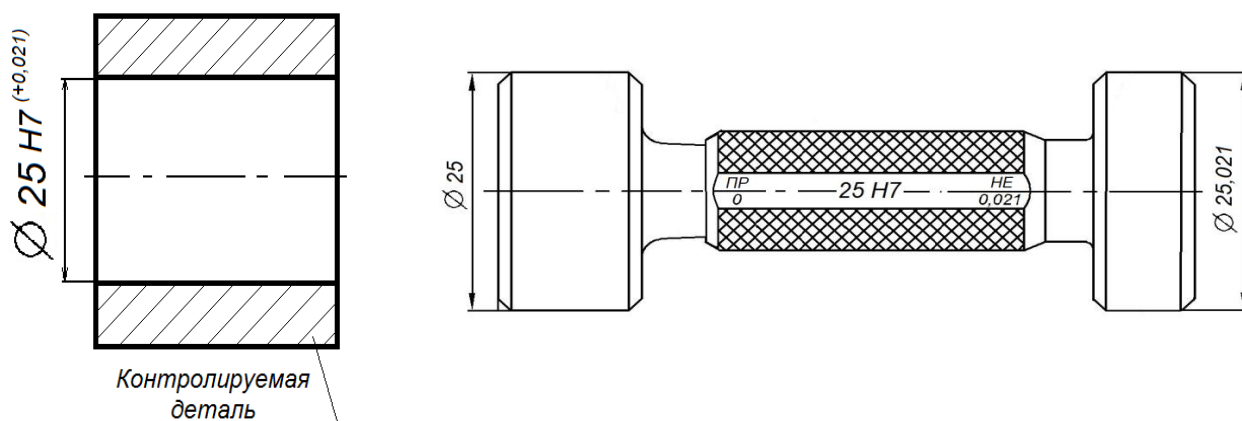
Калибр-пробка для контроля внутренних размеров
